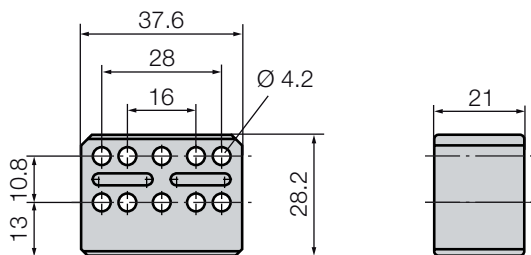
位置指示器BTL6-A-3800-2安装尺寸
